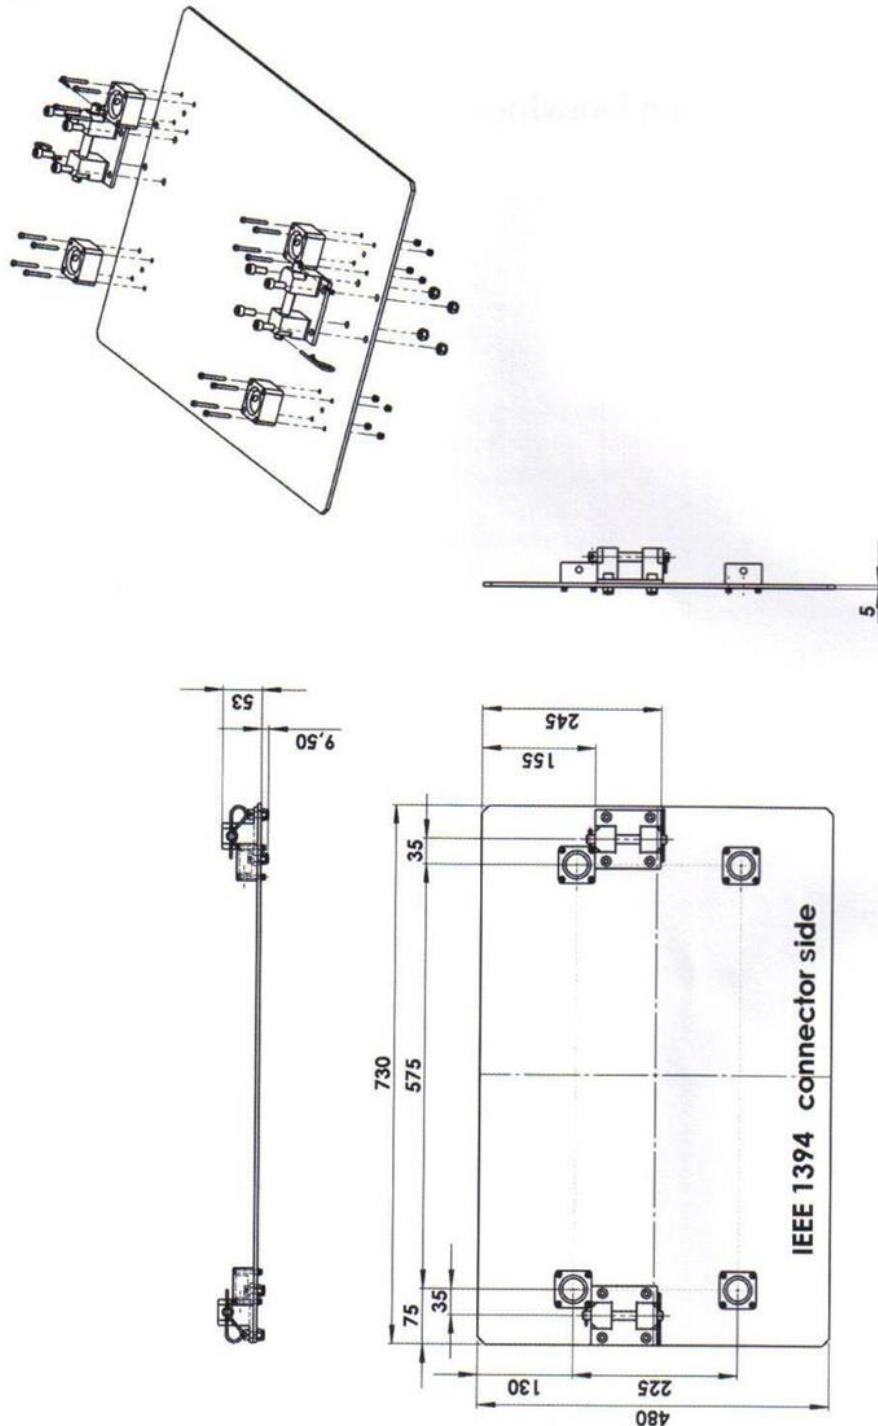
Dimensiones del plato adaptador de la SCU (dimensiones en mm)
